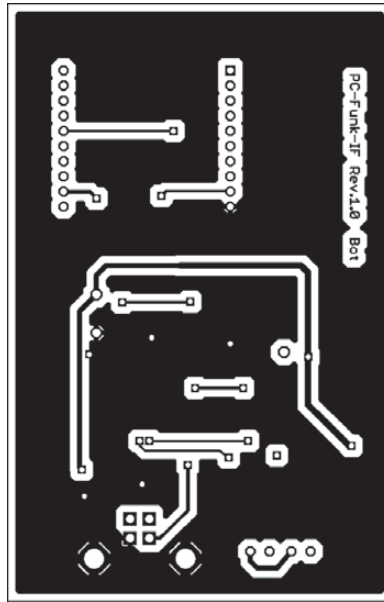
Layoutunterseite des USB-Interfaces; Maßstab 1:1
